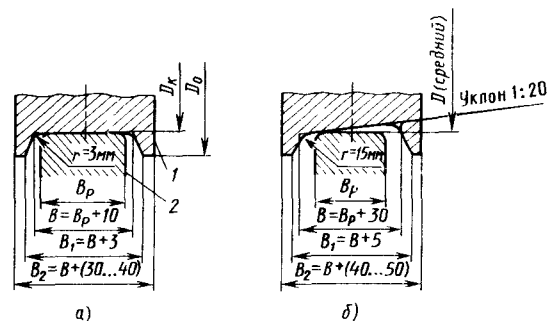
Профили обода ходового цилиндрического (а) и конического (б) колеса с ребрами: 1 — колесо; 2 — рельс
